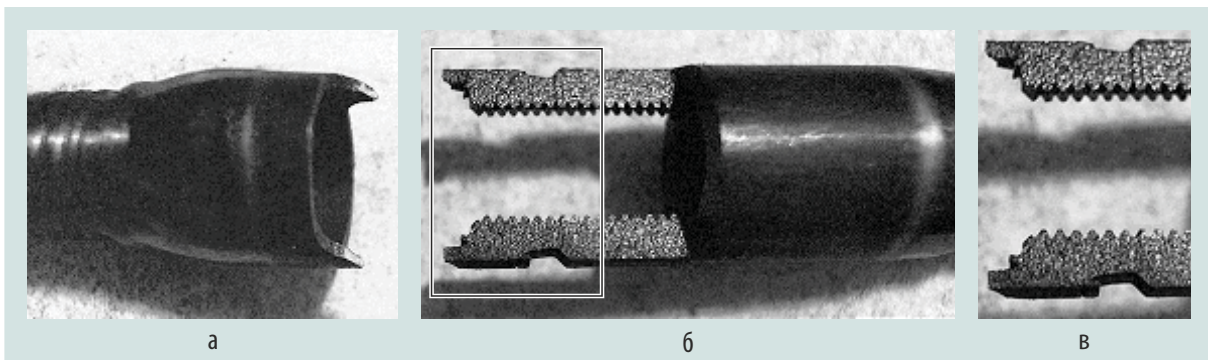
Внешний вид (а, б, в) образца сварного соединения трубы направляющего канала и наконечника после механических испытаний
